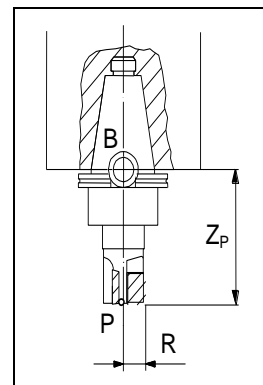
Розташування точки установки інструменту на фрезерному верстаті з ЧПК
